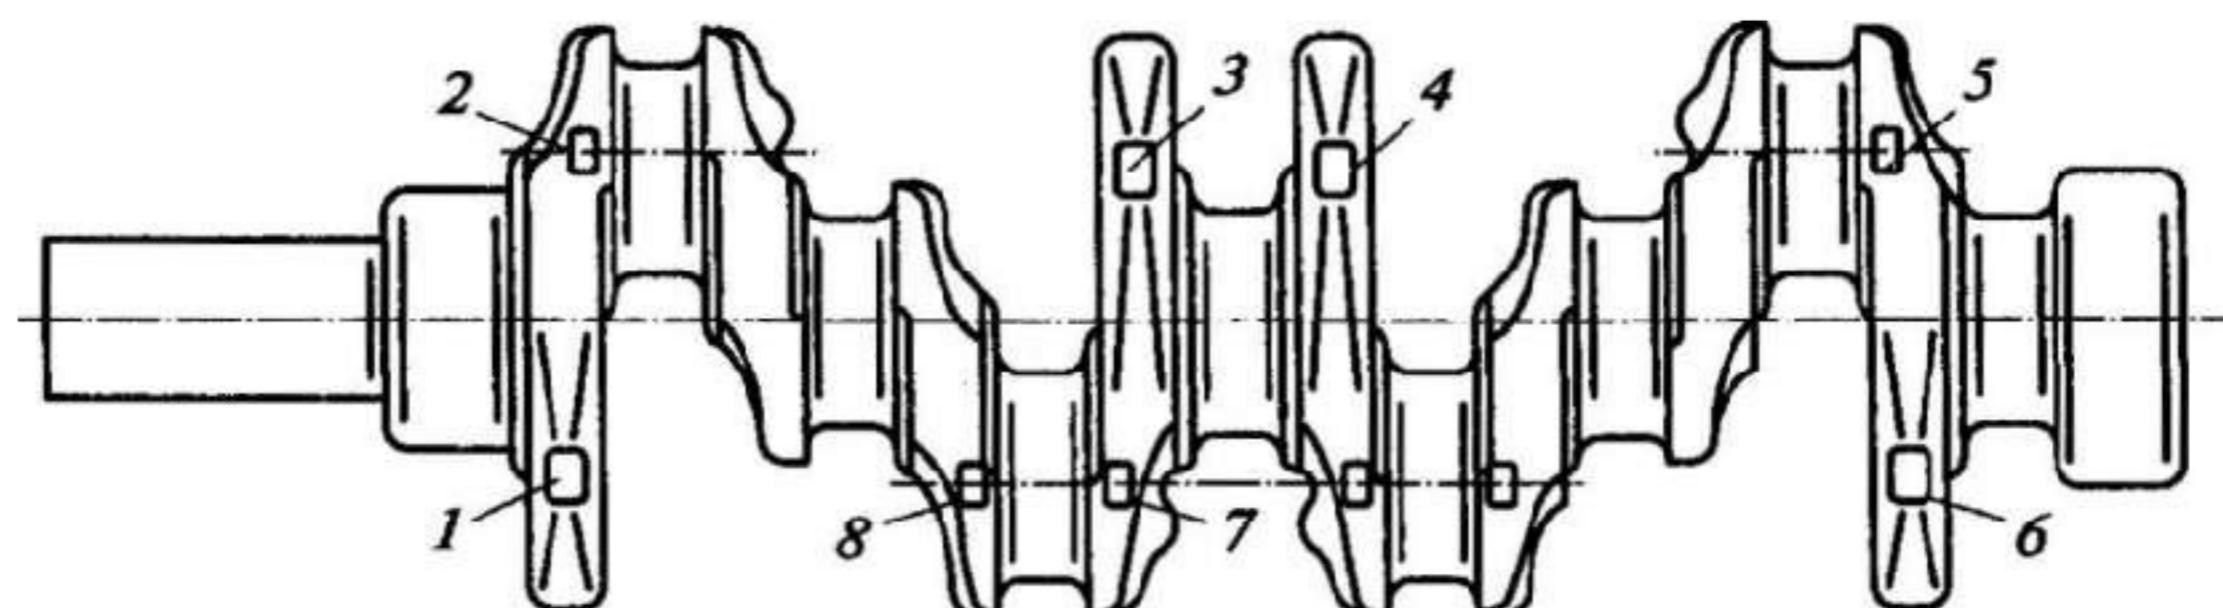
Заготовка коленчатого вала двигателя: 1—8 — опорные технологические площадки
